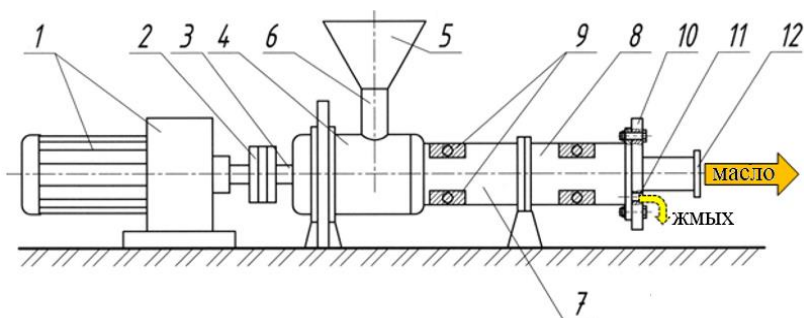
Экспериментальный стенд для получения концентрата ядра семян подсолнечника: 1 мотор-редуктор; 2-муфта; 3-вал шнека; 4-рабочая камера; 5-бункер; 6-канал подачи семян; 7 транспортно-размолочная зона; 8-отжимная зона; 9 нагревательные элементы; 10-матрица 11-отверстия для выхода отжимок; 12-канал для выхода масла
